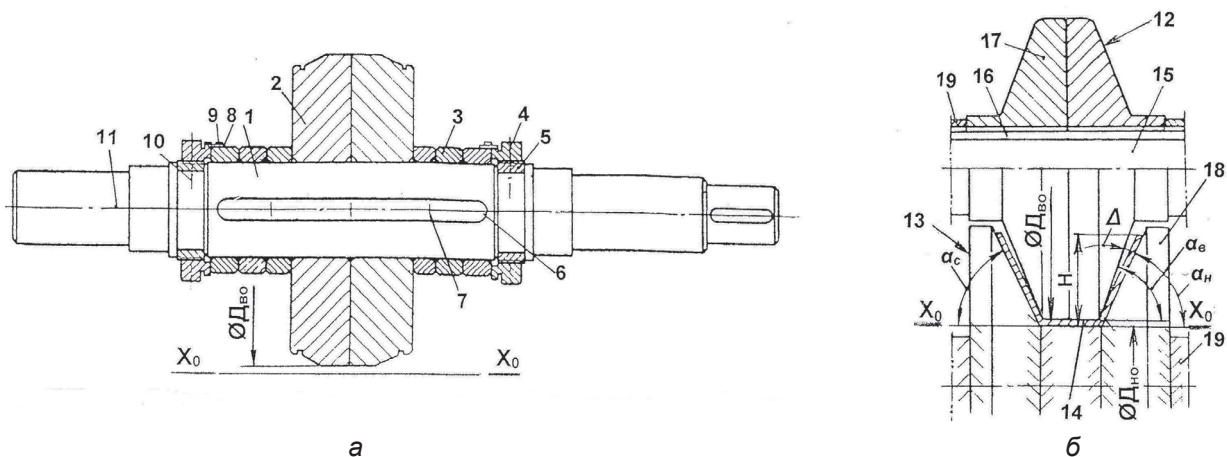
Составной валок профилигибочного стана (а): 1 – рабочий вал; 2 – рабочий формующий дисковый элемент валка; 3 – дистанционный элемент (втулка); 4 – гайка; 5 – составная резьбовая втулка; 6 – шпонка; 7 – винт; 8 – стопорная планка; 9 – винт стопорной планки; 10 – штифт; 11 – ось вращения валка; X_0 - X_0 – уровень формовки и схема сопряжённых по калибру валков для изготовления швеллера в промежуточном проходе (б): 12 – верхний охватываемый валок; 13 – нижний охватываемый валок; 14 – формируемый профиль; 15 – рабочий вал валка; 16 – шпонка; 17 и 18 – формирующие дисковые элементы соответственно верхнего и нижнего валков; 19 – дистанционные цилиндрические элементы (втулки)
